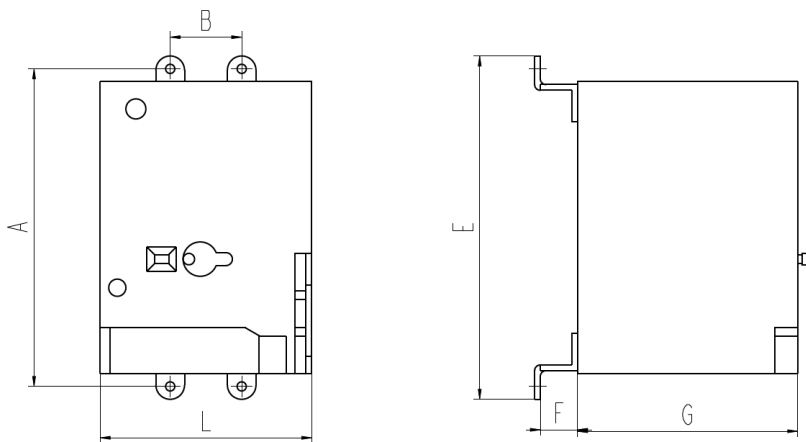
Габаритны и установочные размеры привода моторного МП-300
